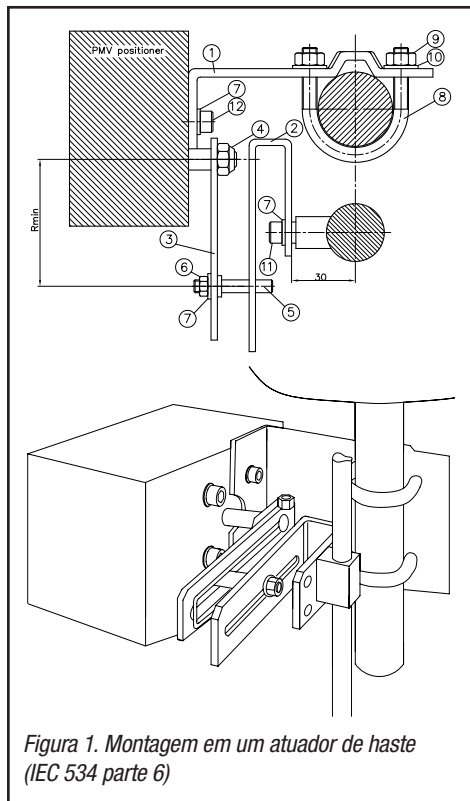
Montagem em um atuador de haste (IEC 534 parte 6)
